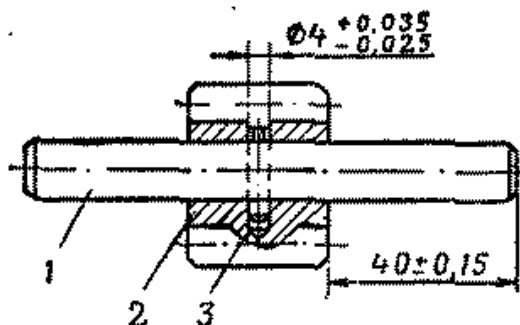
Установка ведущей шестерни верхней секции на валик масляного насоса
